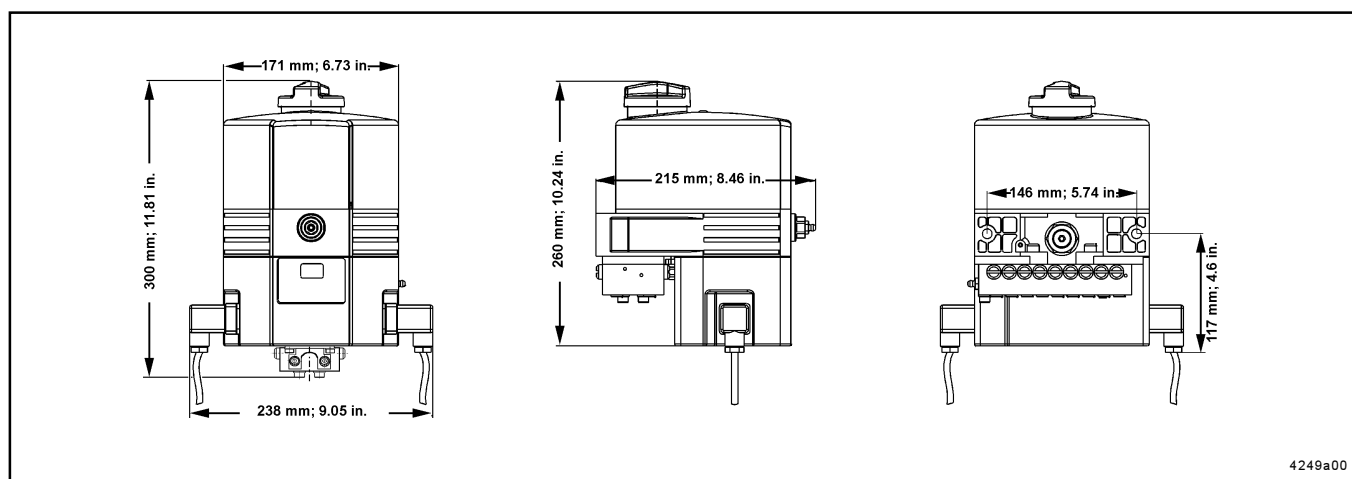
Cotes dimensionnelles de la pompe QLS 311
